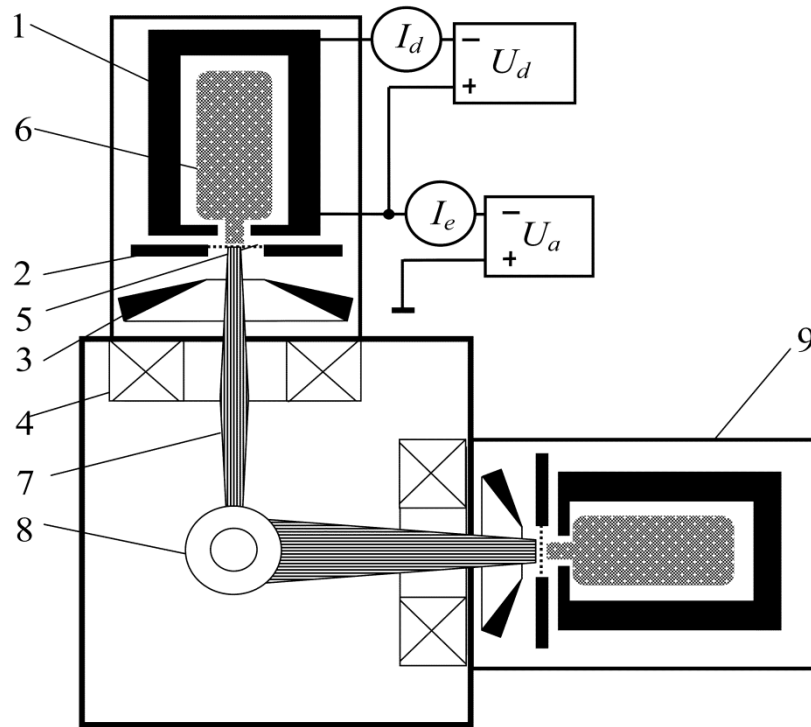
Схема установки для сварки керамических труб: 1 – полый катод; 2 – анод; 3 – ускоряющий электрод; 4 – магнитная фокусирующая система; 5 – эмиссионное окно; 6 – эмиссионная плазма; 7 – электронный пучок; 8 – обрабатываемая деталь; 9 – источник вспомогательного электронного пучка [105].
